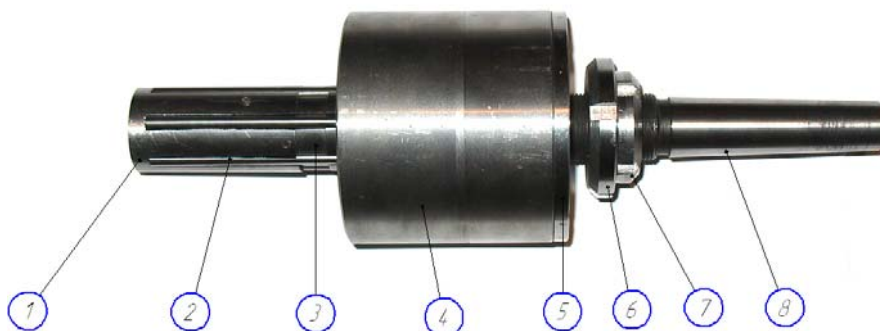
Загальний вигляд роlikової частини інструменту для обробки переривчастих отворів поверхневим пластичним деформуванням: 1 – стакан; 2 – ролик; 3 – сепаратор; 4 – корпус ; 5 – кришка; 6 - гайка регулювальна; 7 – гайка стопорна; 8 – стрижень.
